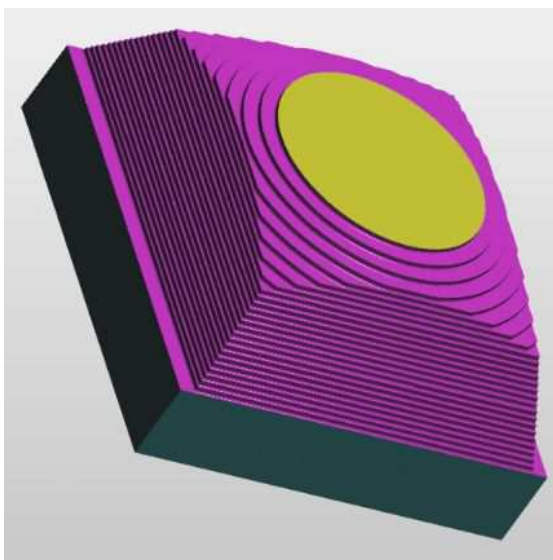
Vyhrubovaná tvarová plocha technologií „Plunge milling“
